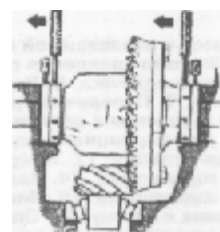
Снимайте монтажные кольца таким образом, чтобы корпус дифференциала принял установочное положение без предварительного натяга
